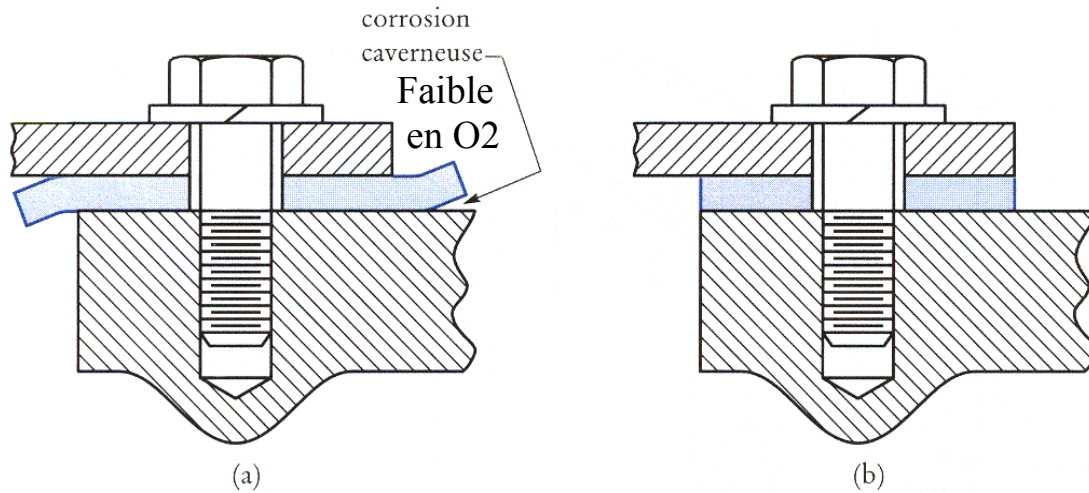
a) Corrosion caverneuse sous un joint trop grand. b) Joint adéquat.
